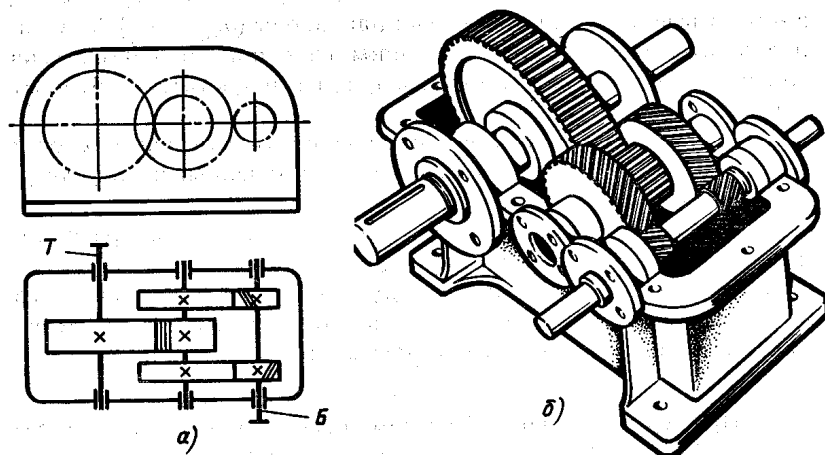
Двухступенчатый горизонтальный редуктор с раздвоенной первой (быстроходной) ступенью: а – кинематическая схема; б – общий вид (без крышки)
